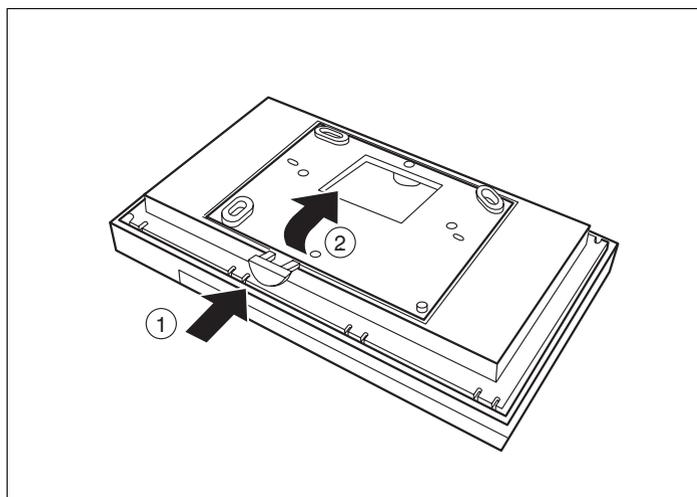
Staccare l'unità di servizio dalla piastra di montaggio
